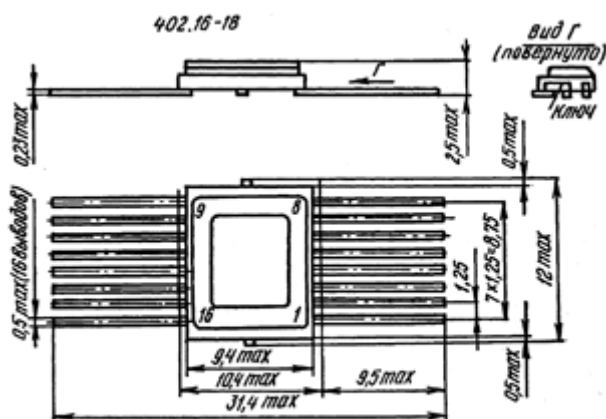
Габаритные размеры корпуса 402.16-18
